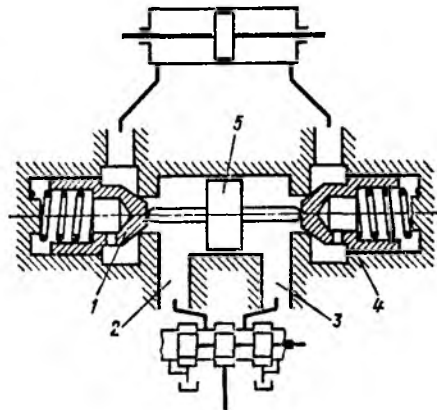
Гидрозамок для фиксации положения поршня гидроцилиндра
